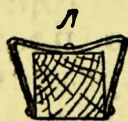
Рычаг *Л* в разрезе (вид спереди) с железными планками с обеих сторон.
